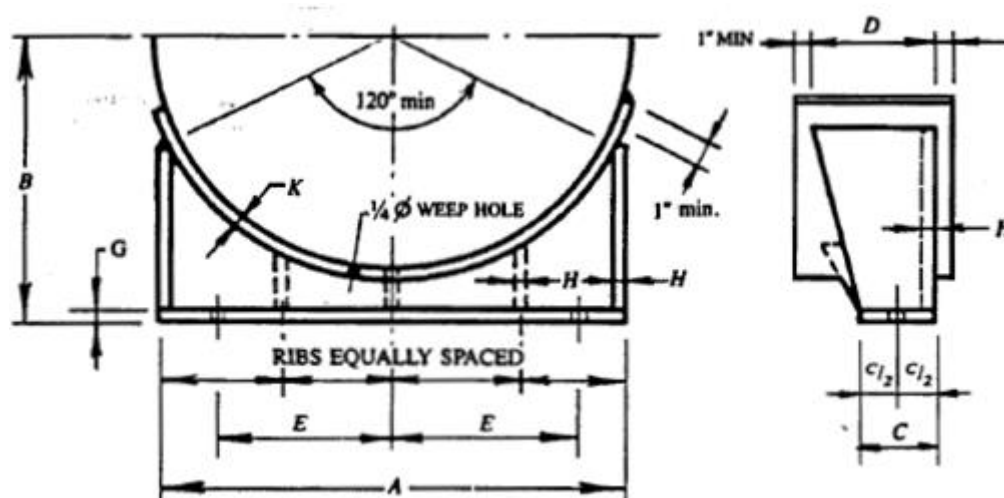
Dimensiones de soportes (Pressure vessel Handbook)
